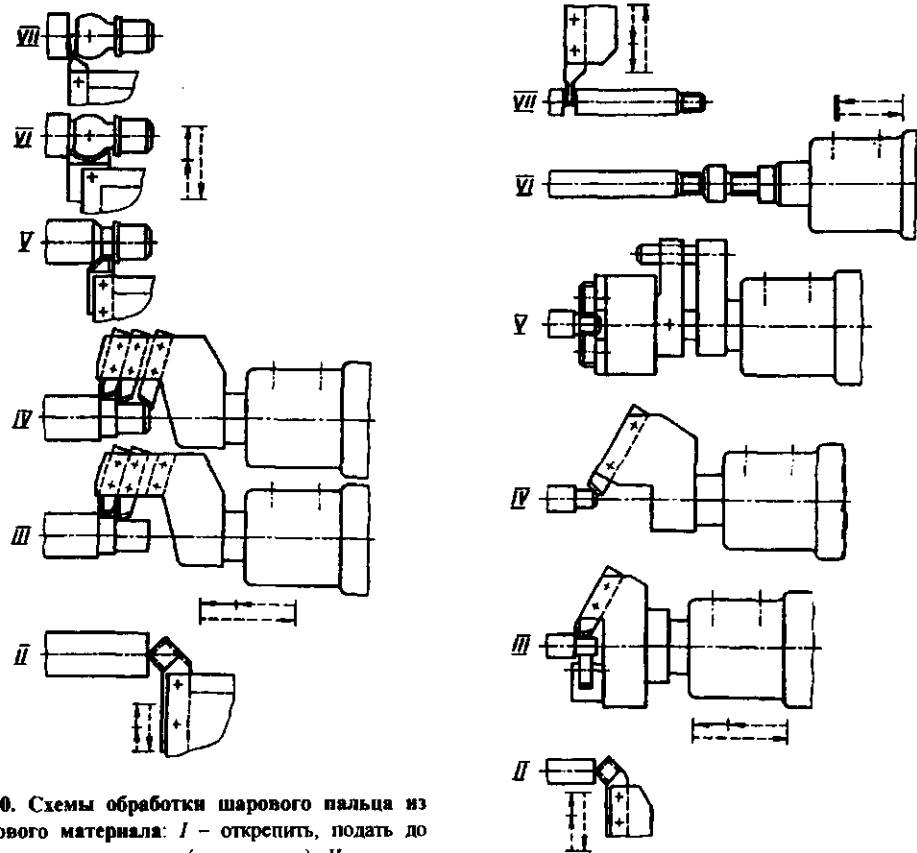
Схемы обработки шарового пальца из пружинного материала: I – открепить, подать до упора и закрепить пруток (не показано); II – подрезать торец; III – обточить стержень по двум диаметрам предварительно; IV – обточить стержень по двум диаметрам окончательно и снять фаску; V – обточить шейку; VI – обточить палец по сфере; VII – отрезать деталь
